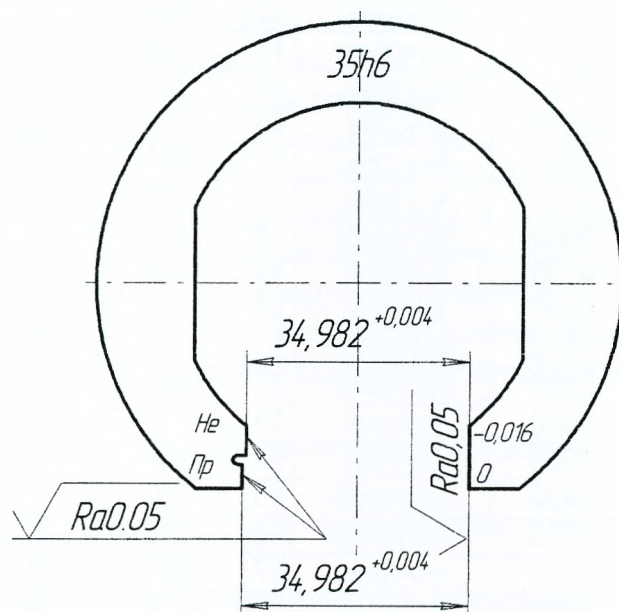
Калибр-скоба для контроля вала 35h7
